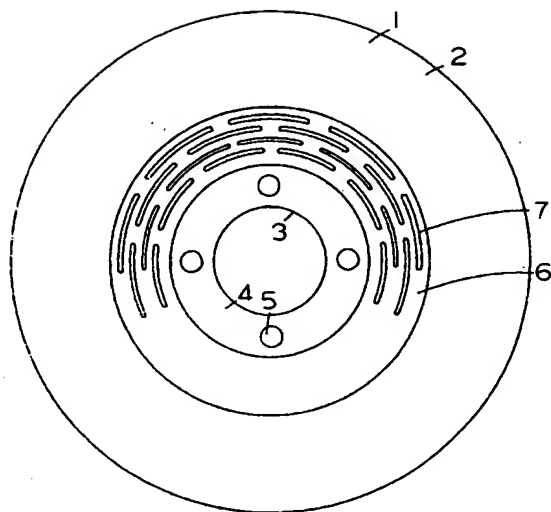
図は第2実施例の平面図、第4図は第3実施例の平面図、第5図はフローティングディスクの平面図である。
